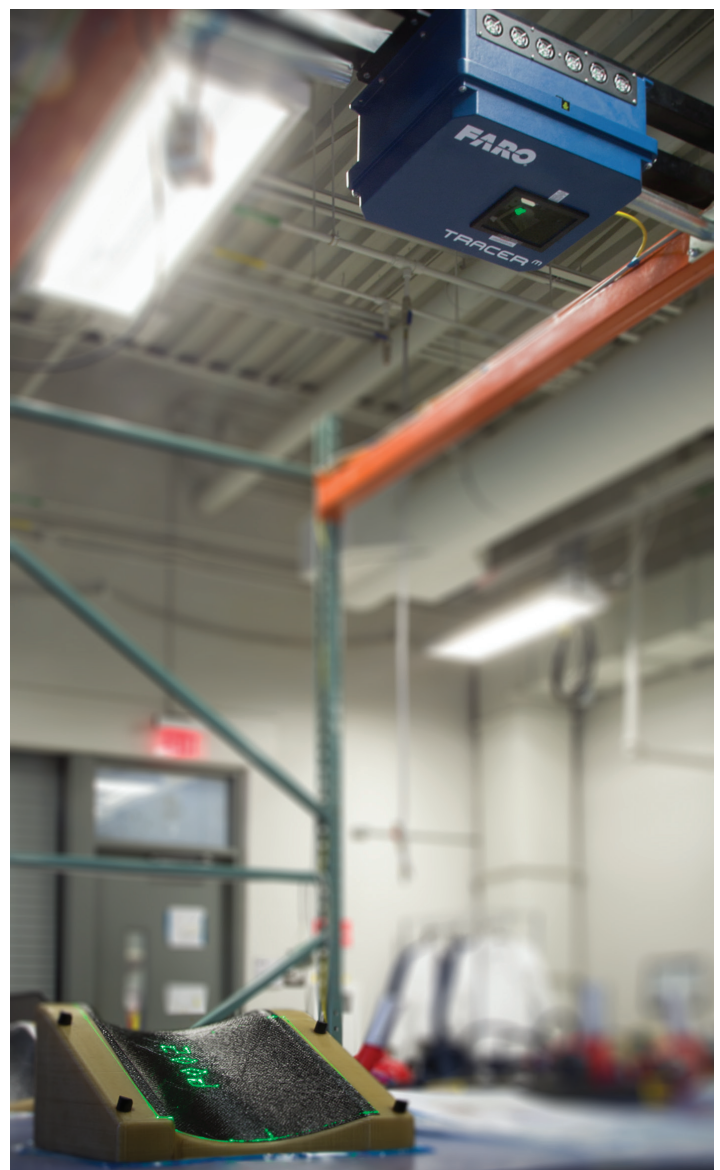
Un Tracer^M proyectando sobre un molde de aleta para el moldeo guiado por láser en un taller de ensamblaje de materiales compuestos
